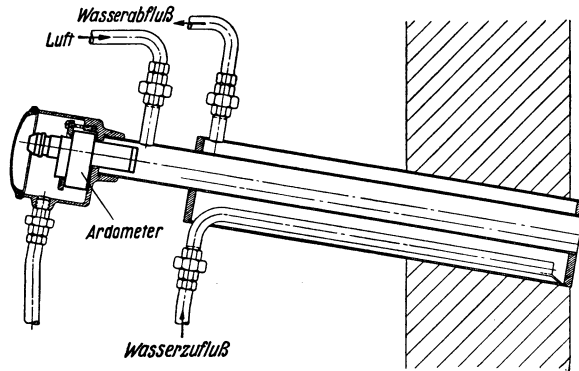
Einbau eines Ardometers in ein Schutzgehäuse (Siemens & Halske).
